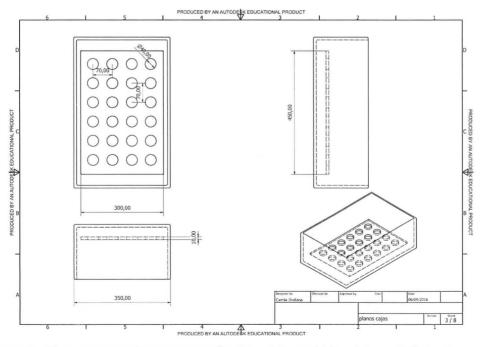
Plano contenedor correspondiente a sistema hidropónico raíz flotante.
